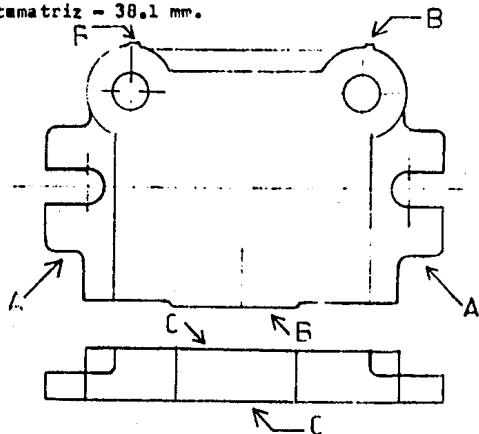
Zapata Inferior con saliente de fijación (A)
